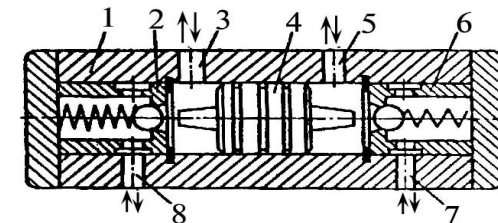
Гідрозамок: 1 – корпус; 2 і 6 – зворотні клапани; 3, 5, 7 і 8 – клапани; 4 – поршень.
